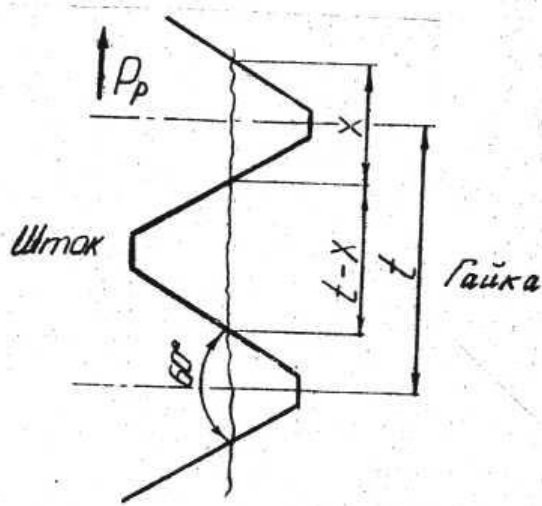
Розрахункова схема різьби штока на зріз
